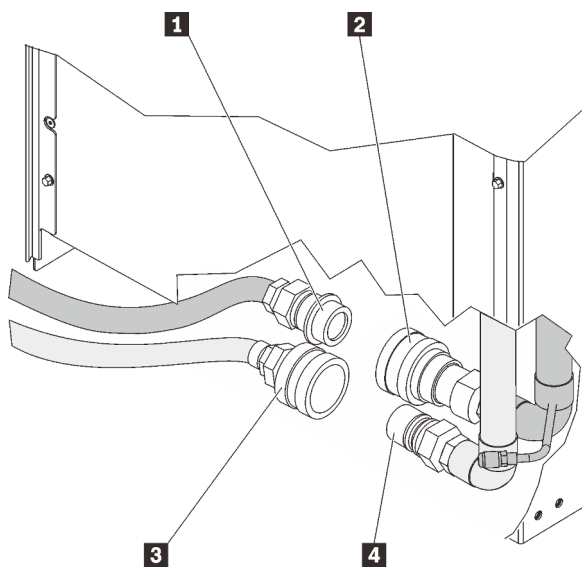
Подающий и возвратный шланги и муфты коллектора
